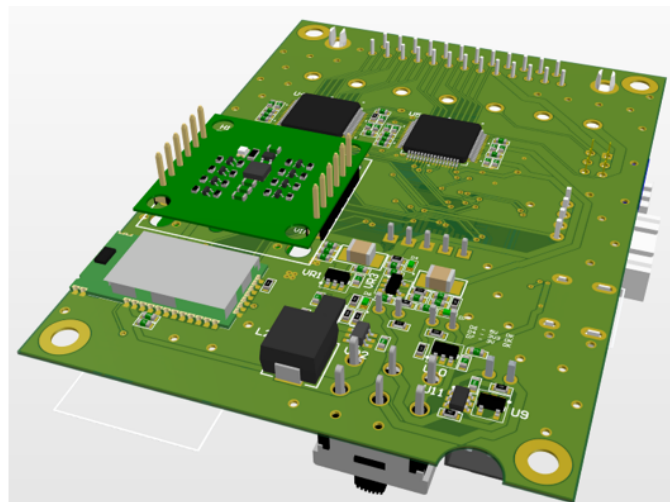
Modelo 3D de la capa inferior de la PCB
